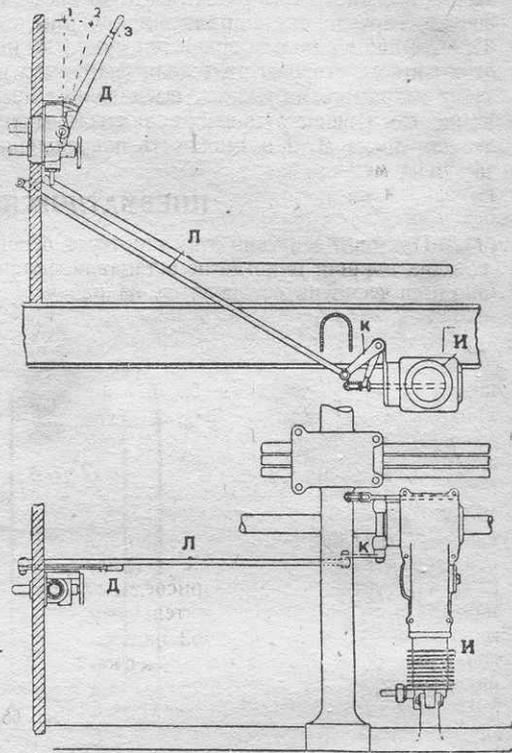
Установка на автомобиле пневматического пускового приспособления «Заурер».
